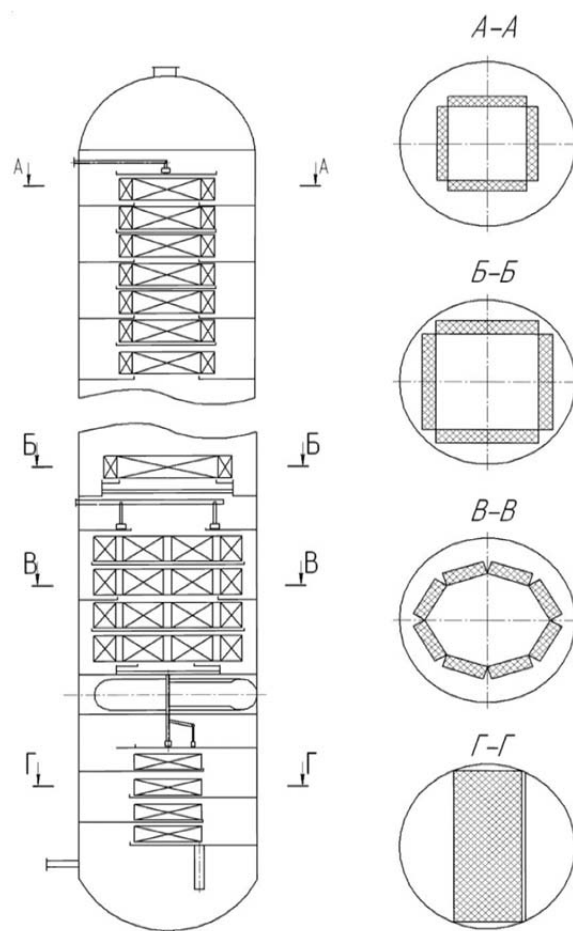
Схема вакуумной колонны с модулями перекрестноточной насадки
